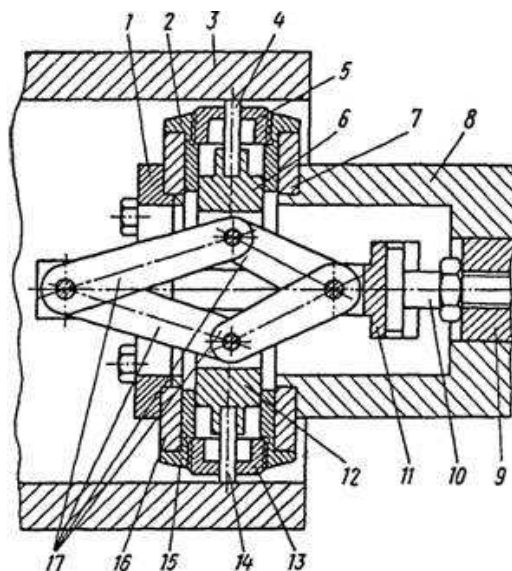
Приспособление для обработки рабочей поверхности гильз блока цилиндров
